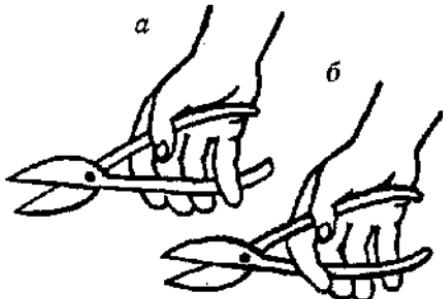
Как держать ножницы по металлу: а — хватка с разжиманием ножниц мизинцем; б — хватка с разжиманием ножниц указательным пальцем.
